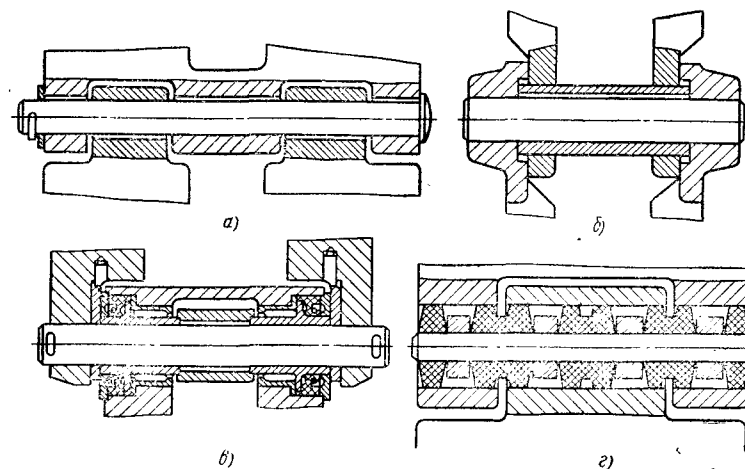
Пальцевые шарниры: а — открытый пятипроушинный; б — закрытый; в — на игольчатых подшипниках; г — на резиновых втулках
